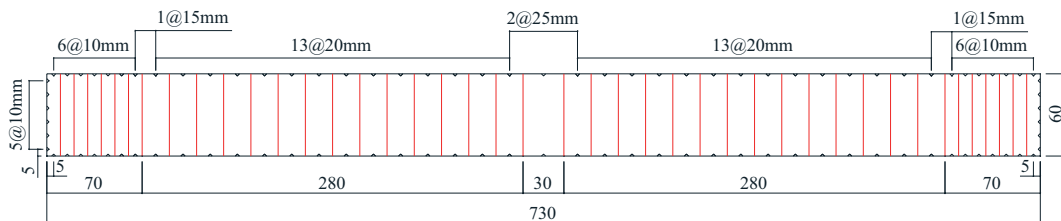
Vue en coupe d'un spécimen de type oxycoupage de type T1 (en mm).
